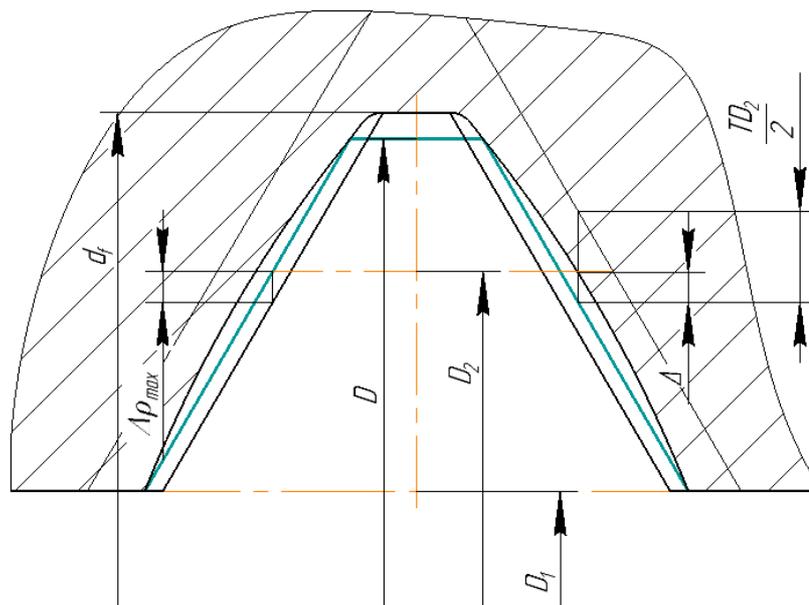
Сравнение номинального профиля резьбы и профиля, полученного при моделировании процесса резьбофрезерования: $\Delta\rho_{\max}$ – величина геометрической погрешности профиля; Δ – величина прогиба боковых сторон; D – номинальный диаметр внутренней резьбы; D_1 – внутренний диаметр резьбы; D_2 – средний диаметр резьбы; TD_2 – поле допуска на средний диаметр резьбы.
